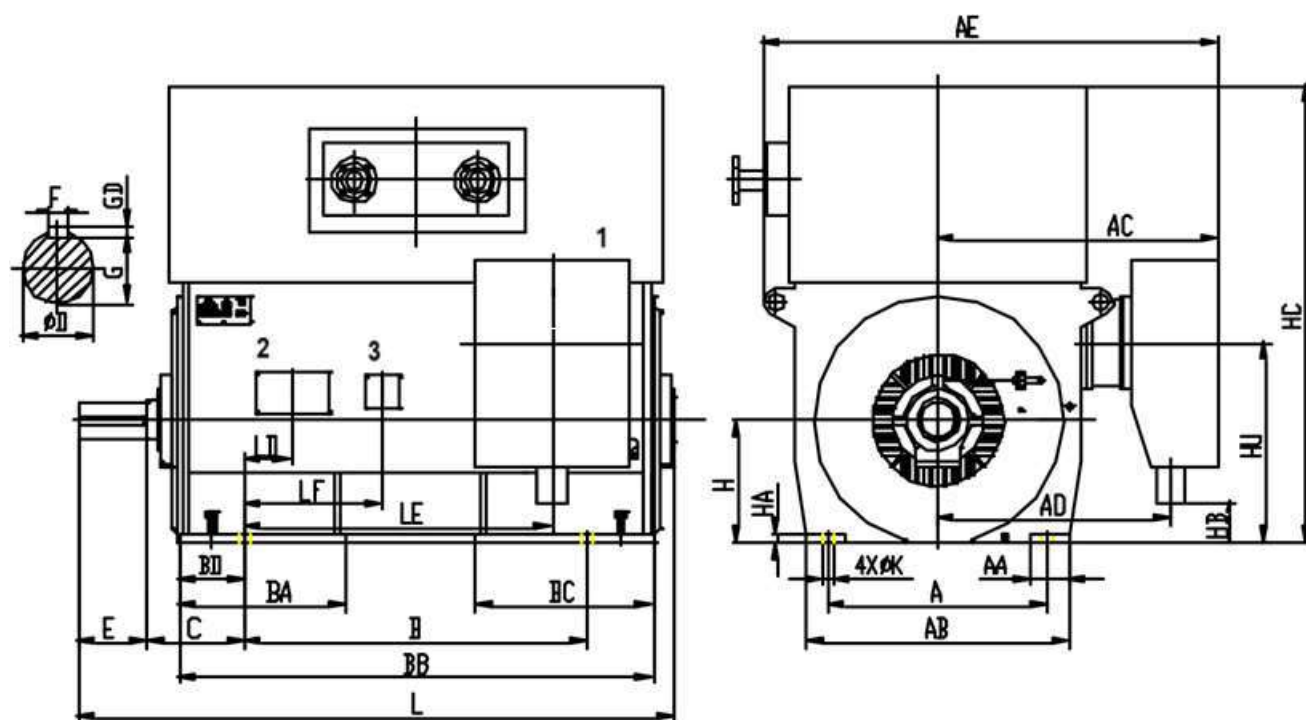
Установочные размеры двигателей серии YZYKS (поз.1 – главная коробка выводов, поз.2 – коробка выводов термодатчиков, поз.3 - коробка выводов обогревателя)
